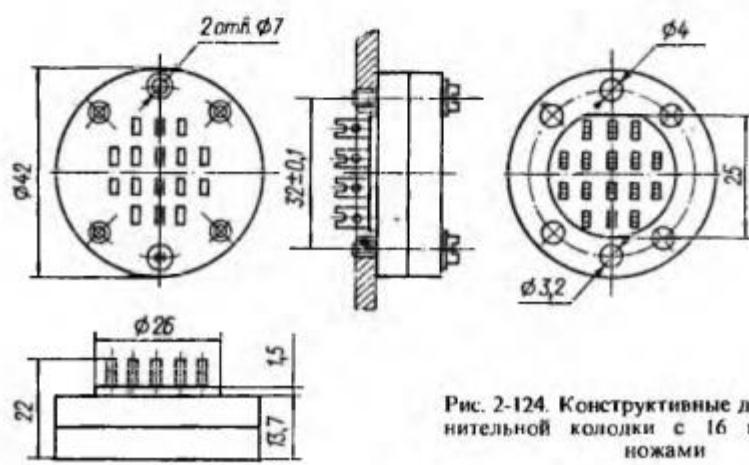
Конструктивные данные соединительной колодки с 16 контактными ножами
